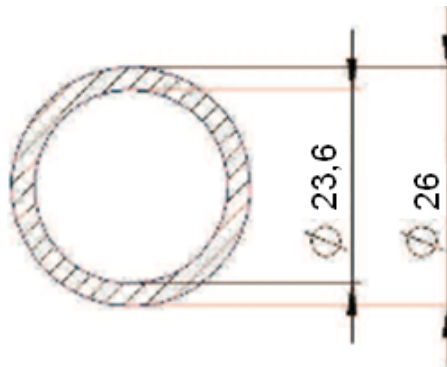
Dimensiones geométricas mínimas del tubo de acero estándar
